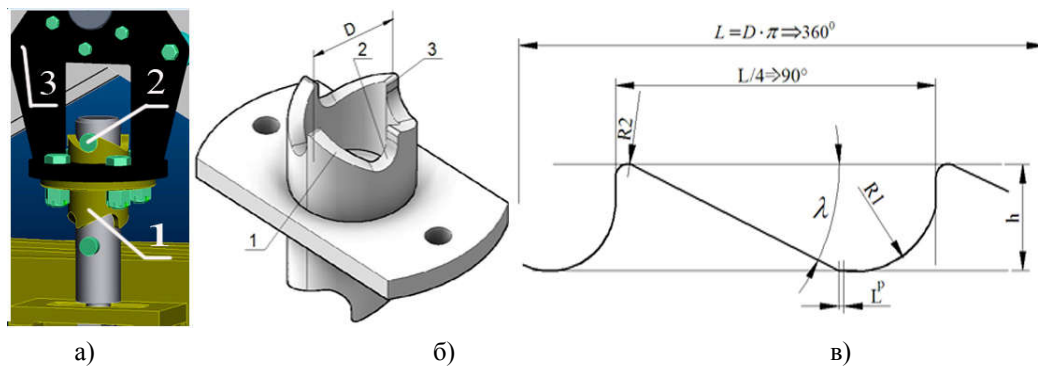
Замковое устройство механизма (а), входящий в него цилиндрический кулачок (б) и его развертка (в)
